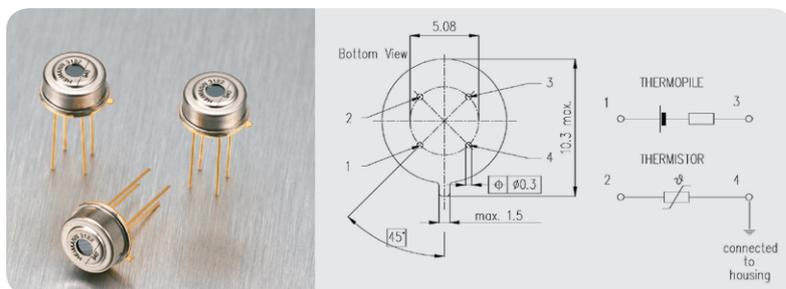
Der Thermopile-Sensor TPS 334 mit Anschlussbelegung und Innenschaltung
